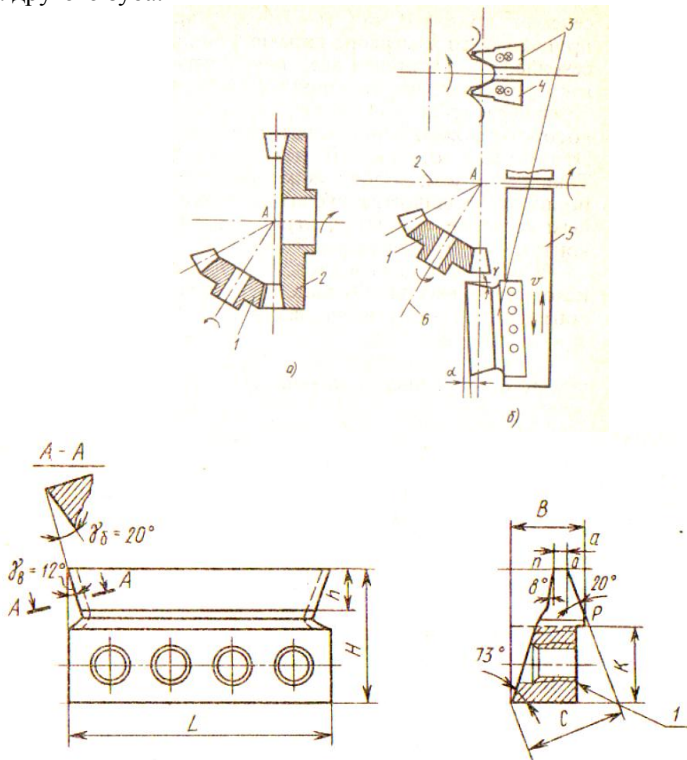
Схема нарезания прямозубого конического колеса зубострогальными резцами. Зубострогальный резец
